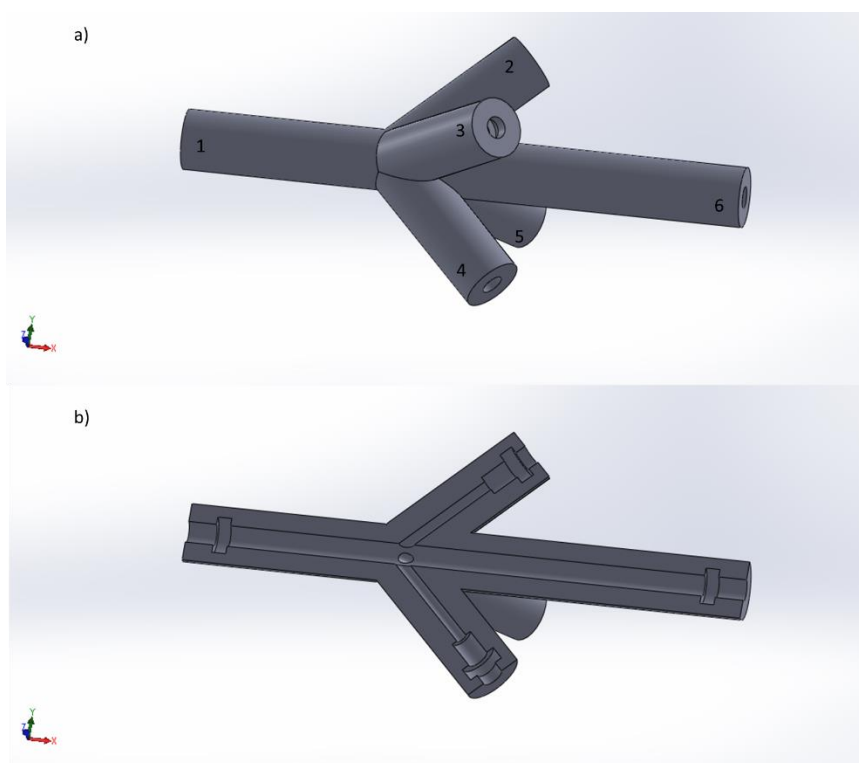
a) vista tridimensional de la pieza 2 (Anexo I); b) corte transversal de la misma.
